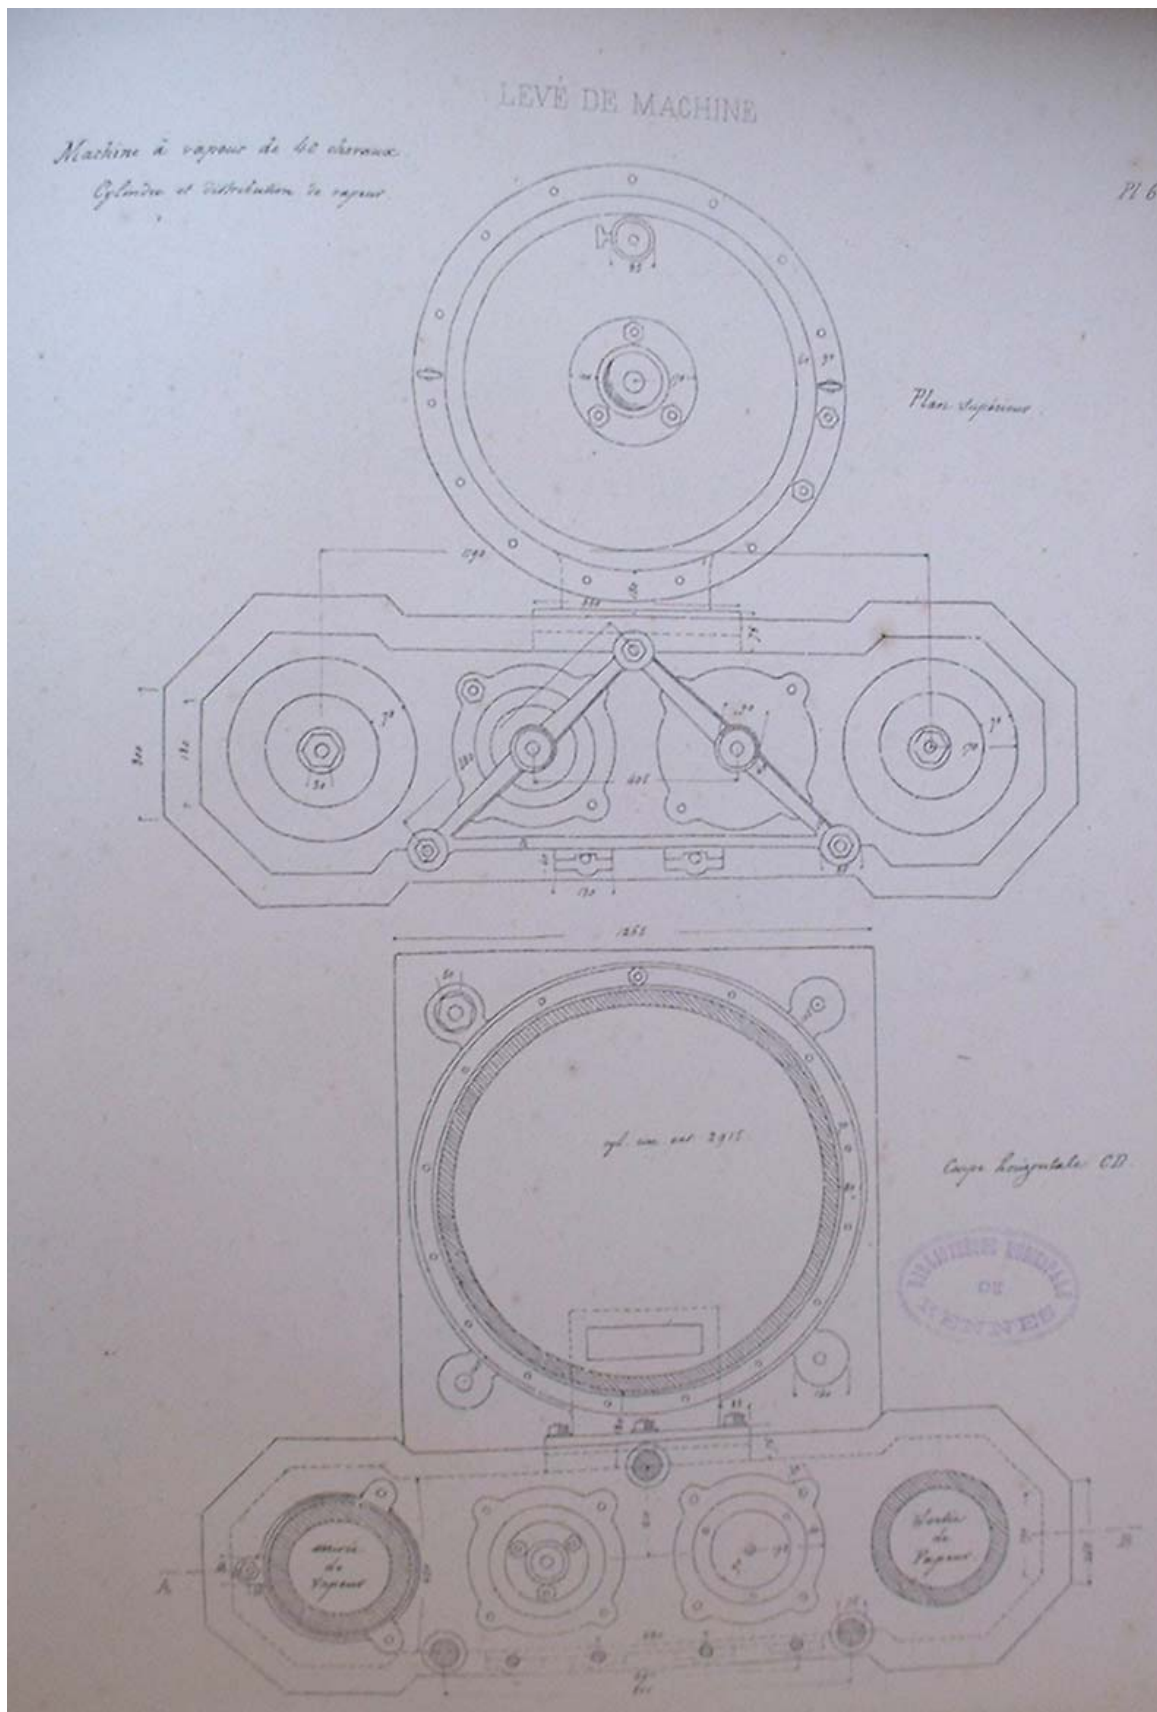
, sous-ensemble, machine à vapeur, Tronquoy, 35 x 20 cm.
